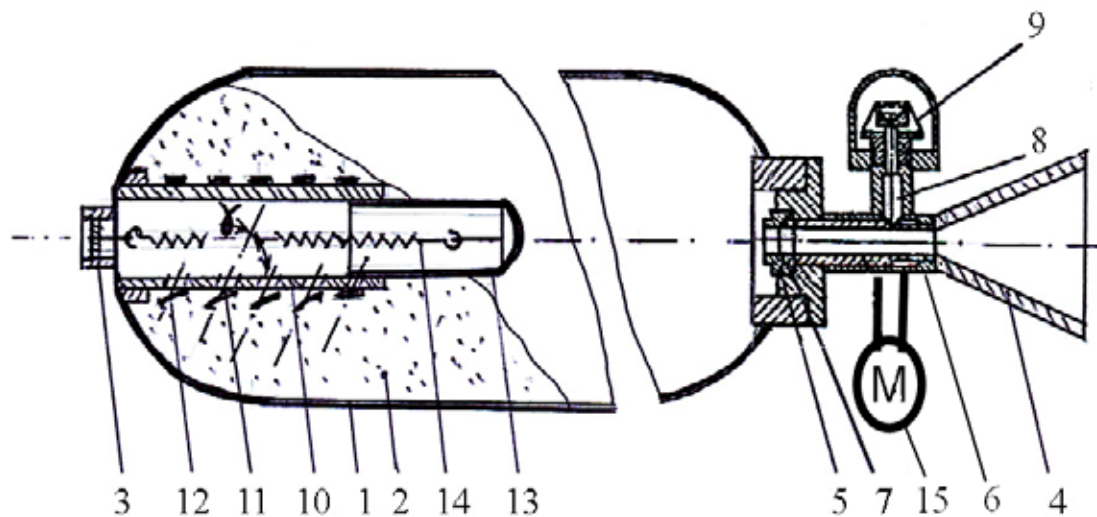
Схема конструкции автоматического порошкового огнетушителя ОПШ-20-Б: 1 – резервуар, 2 – огнетушащий порошок, 3 – зарядный клапан, 4 – сопло для выпуска газопорошковой смеси, 5 – запорно-пусковое устройство, 6 – подвижная втулка, 7 – герметичная мембрана, 8 – шток, 9 – термочувствительная нить, 10 – газоаккумулятор, 11 – отверстия, 12 – обратные клапаны, 13 – подвижный корпус, 14 – пружина, 15 – манометр.
